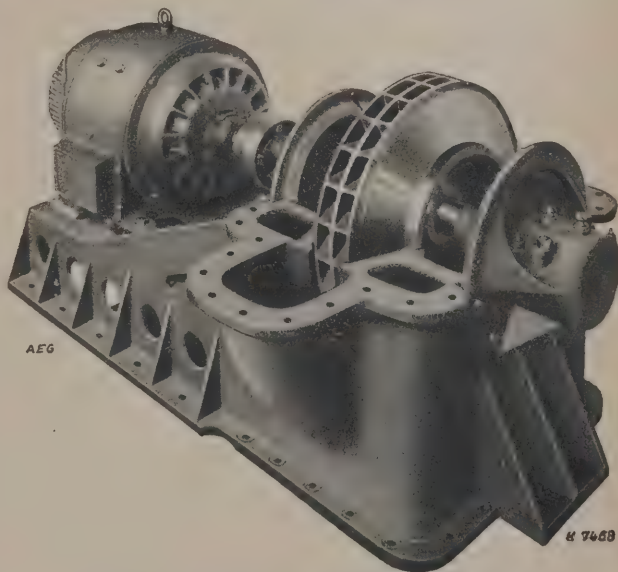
Turbogebläse mit Elektromotor geöffnet.
